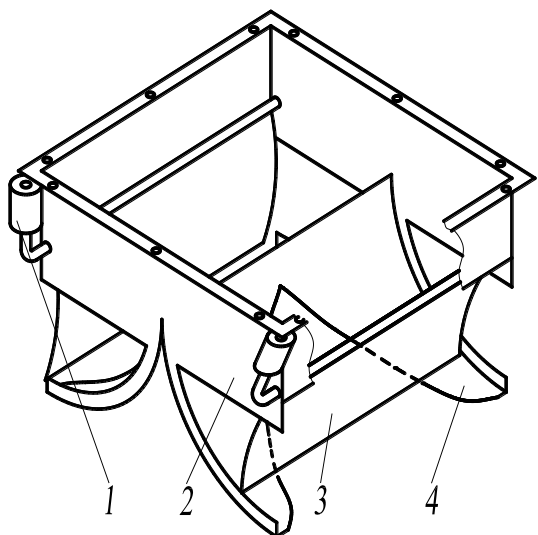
Схема экспериментального образца двухсекционного регулятора расхода воздуха: 1 – противовес; 2 – плоская стенка корпуса; 3 – створка; 4 – криволинейная стенка корпуса
